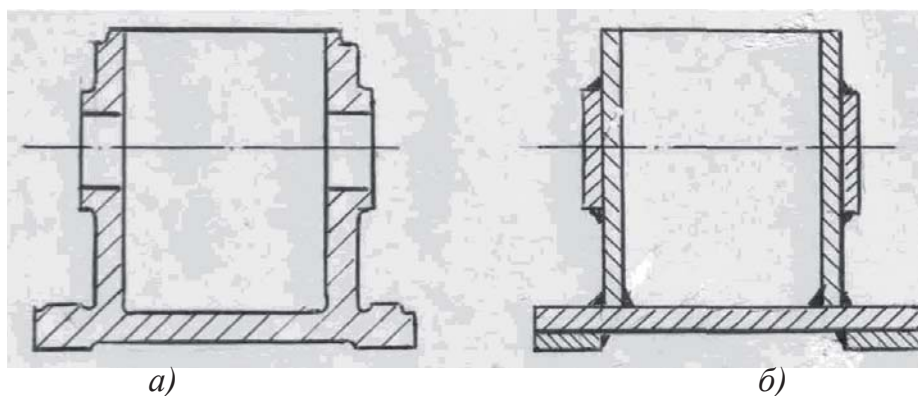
Два вида заготовок, применяемые для изготовления корпусной детали при различной серийности производства: *а* – заготовка-отливка; *б* – сварная заготовка
